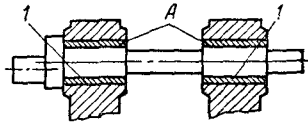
Приспособление для проверки параллельности направляющих пресса.
